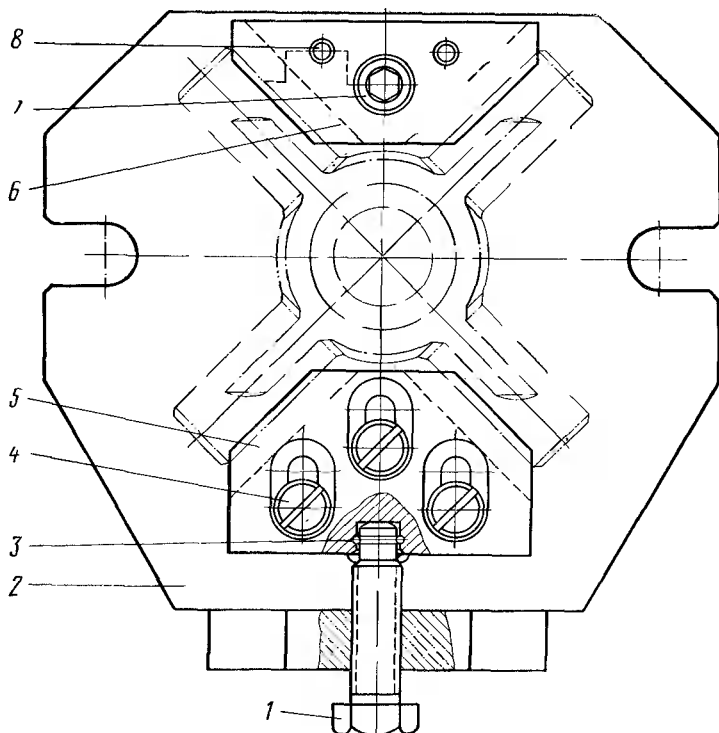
Приспособление для фрезерования лысок на шинах крестовины дифференциала:
